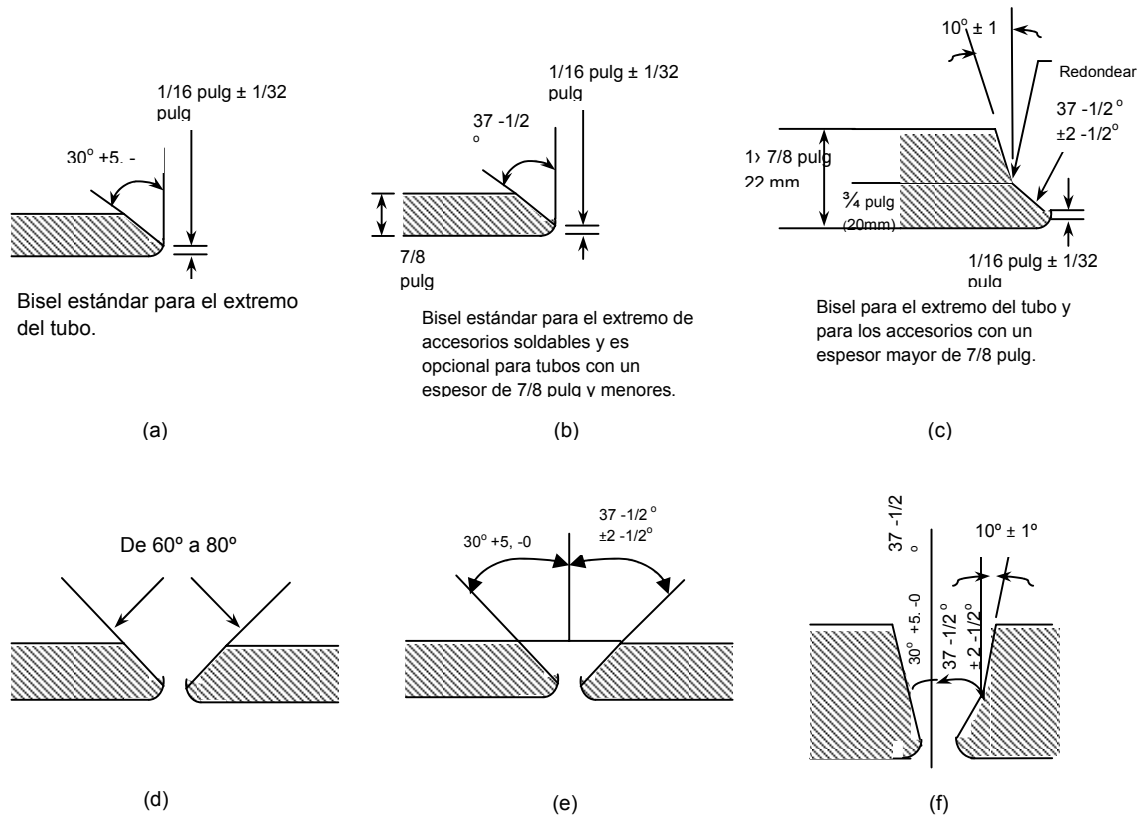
Diseño del bisel en la junta de soldadura para tubos de igual espesor de pared [7].
